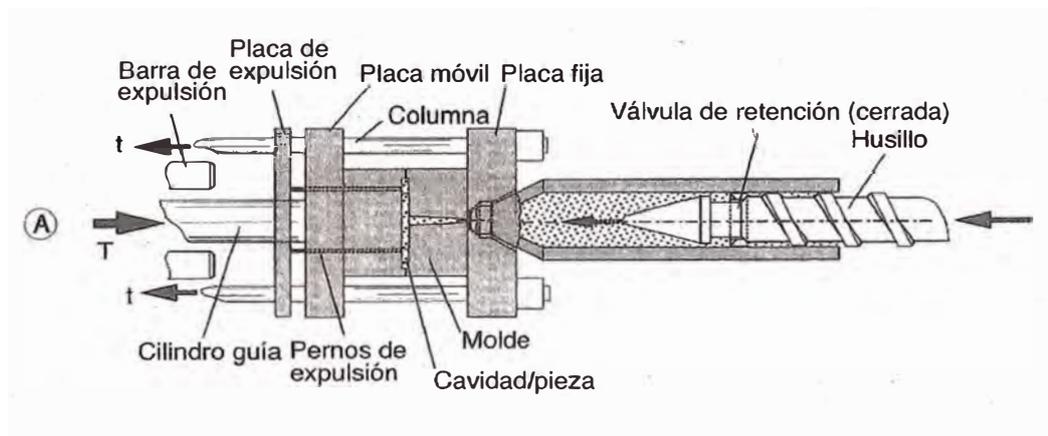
INYECCIÓN DEL PLÁSTICO DENTRO DEL MOLDE
